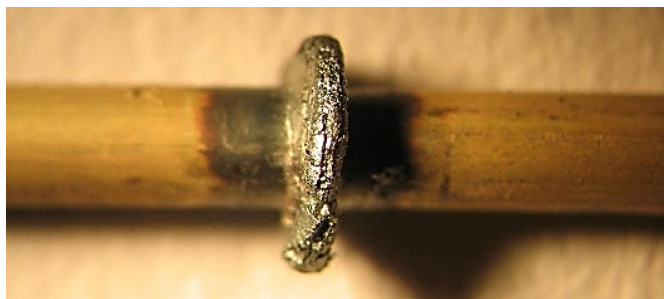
Внешний вид сварного соединения с гратом латунированной проволоки после стыковой сварки сопротивлением, $\times 6$
